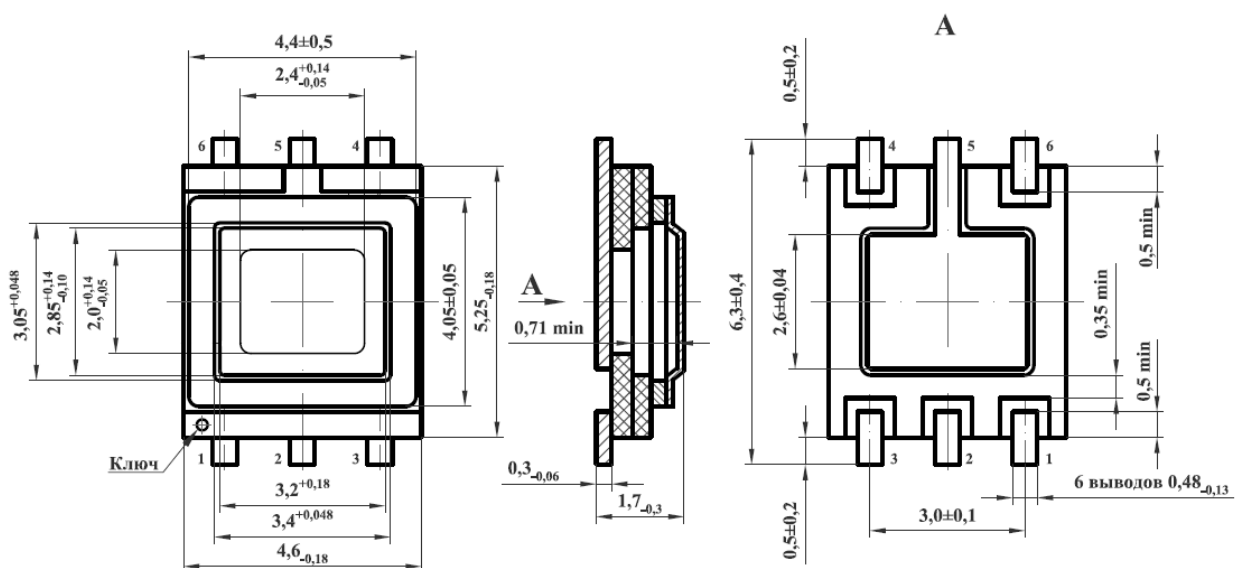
Габаритный чертёж корпуса 5221.6-1 (размеры в мм)
